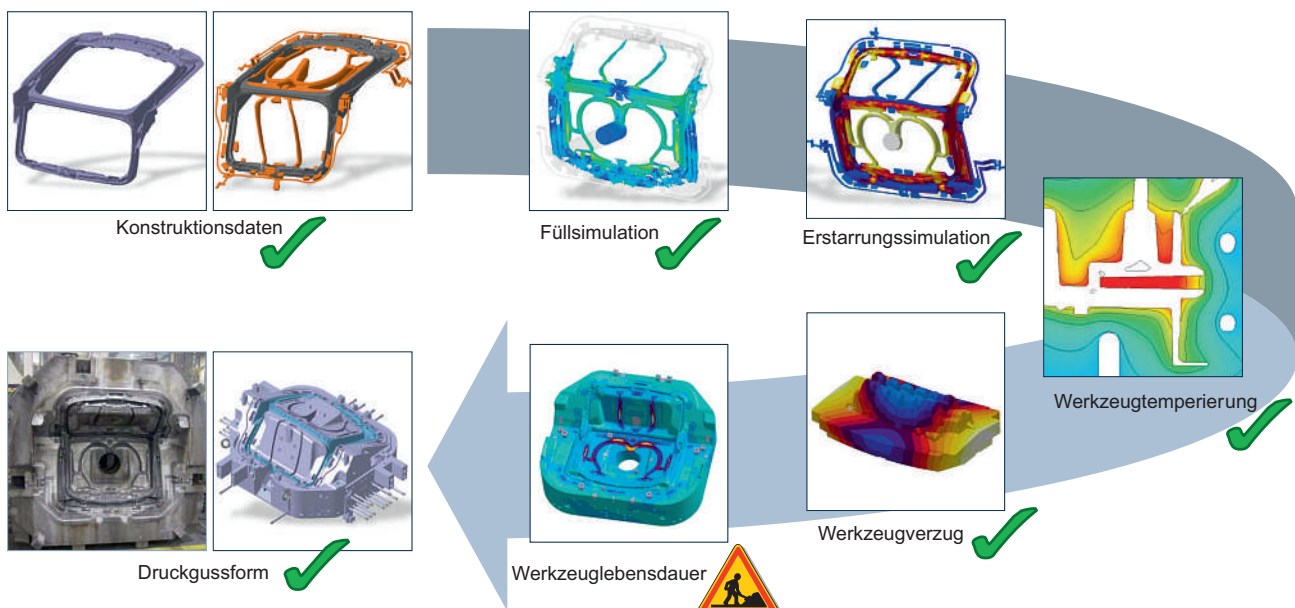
Virtuelle Auslegung der Druckgießwerkzeuge
